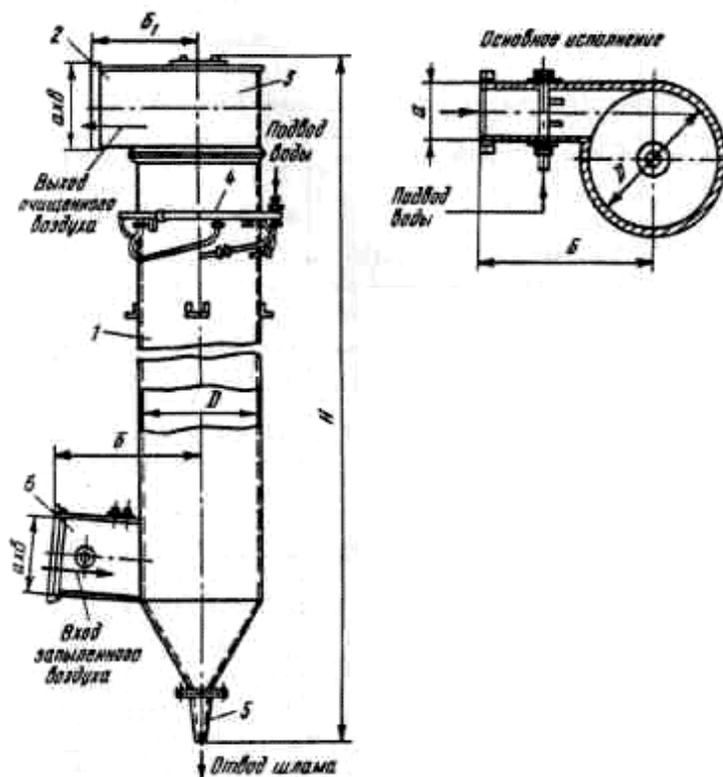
Циклон с водяной пленкой ЦВП: 1 — корпус; 2 — выходной патрубок; 3 — улитка; 4 — коллектор; 5 — конусный патрубок (гидрозатвор); 6 — входной патрубок.
